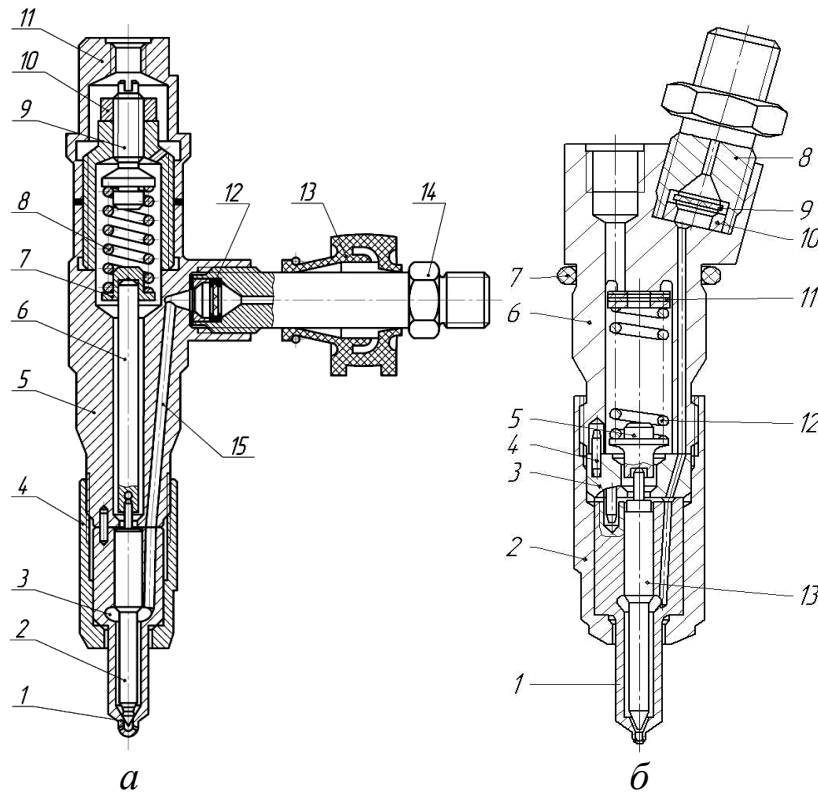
Форсунка штанговая (*а*): *1* – сопловые отверстия; *2* – игла; *3* – корпус распылителя; *4* – гайка распылителя; *5* – корпус; *6* – шток; *7* – опорная шайба; *8* – пружина; *9* – регулировочный винт; *10* – контргайка; *11* – колпак; *12* – сетчатый фильтр; *13* – уплотнитель; *14* – штуцер; *15* – канал
